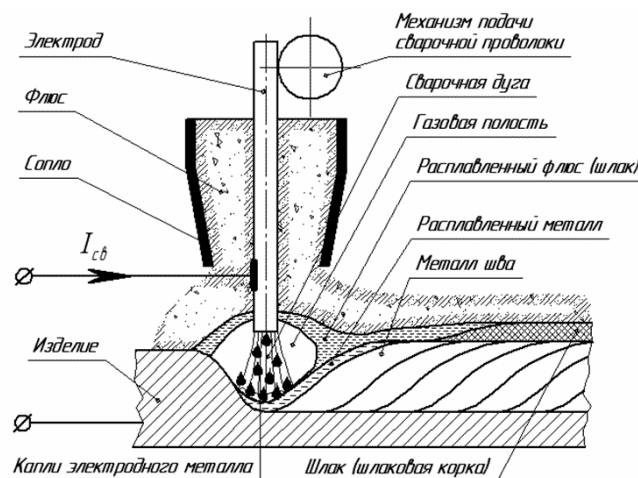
Схема автоматической сварки под слоем флюса
